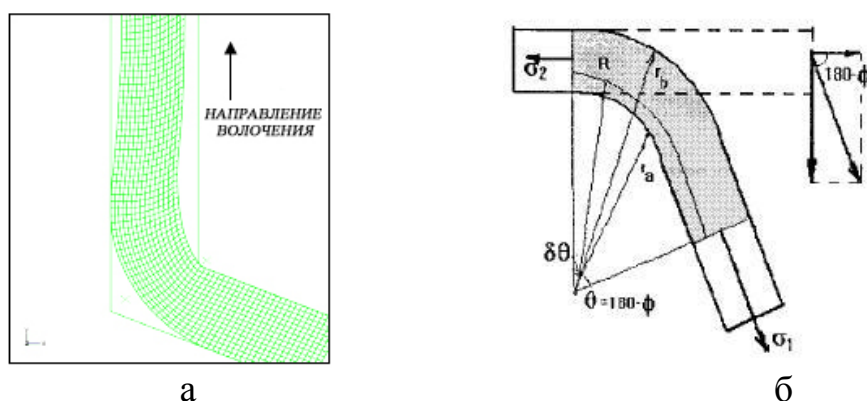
Схематическое изображение подачи заготовки в процессе непрерывного равноканального многоуглового прессования
